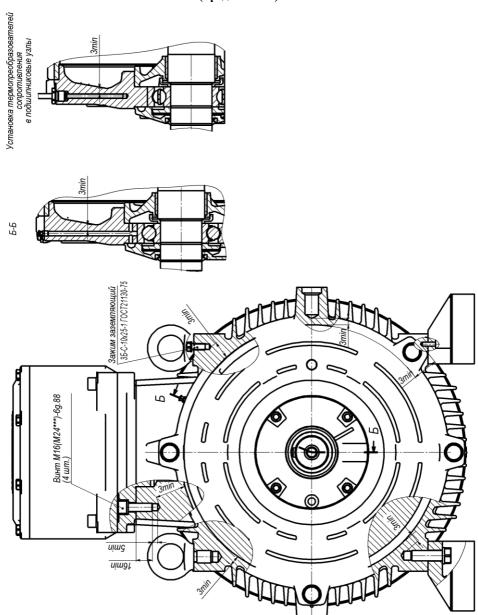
Чертеж взрывозащиты двигателей BA(B),1PBA280M,315,355; BRA(B),1PBRA 315,355
